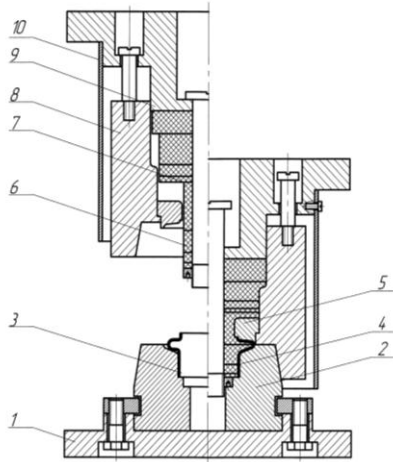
Схема штампа для калибровки облегченных фланцев: 1 – плита; 2 – нижняя полуматрица; 3 – фланец с предварительным гофром; 4 – фланец с откалиброванным гофром; 5 – верхняя полуматрица; 6 – пуансон эластичный; 7 – прижим эластичный; 8 – корпус; 9 – пуансон жесткий; 10 – крышка
